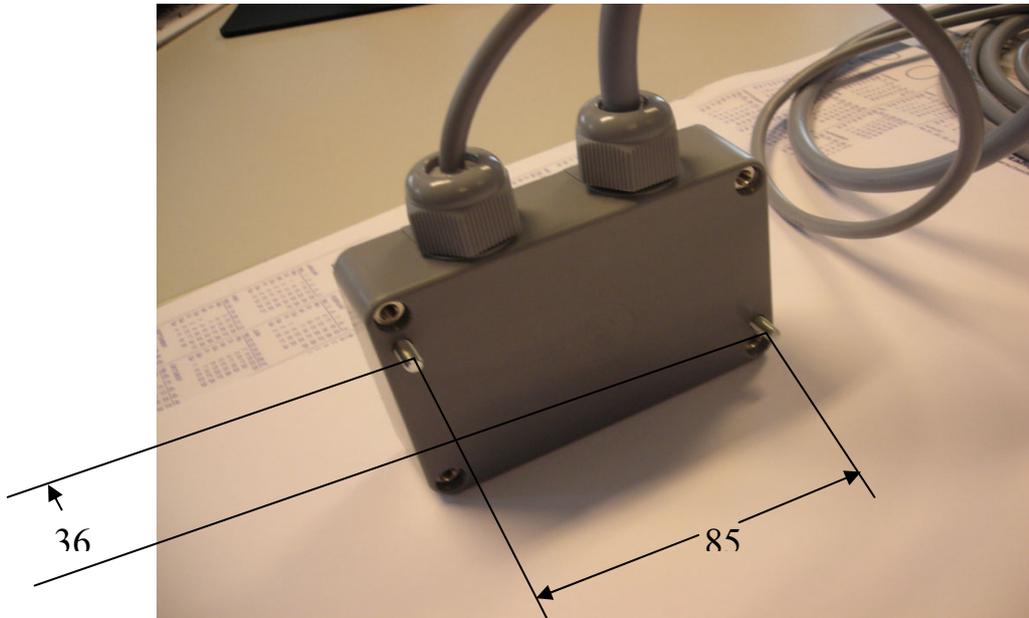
Maße der Befestigungsschrauben (Befestigung mit 2 Schrauben M4)
